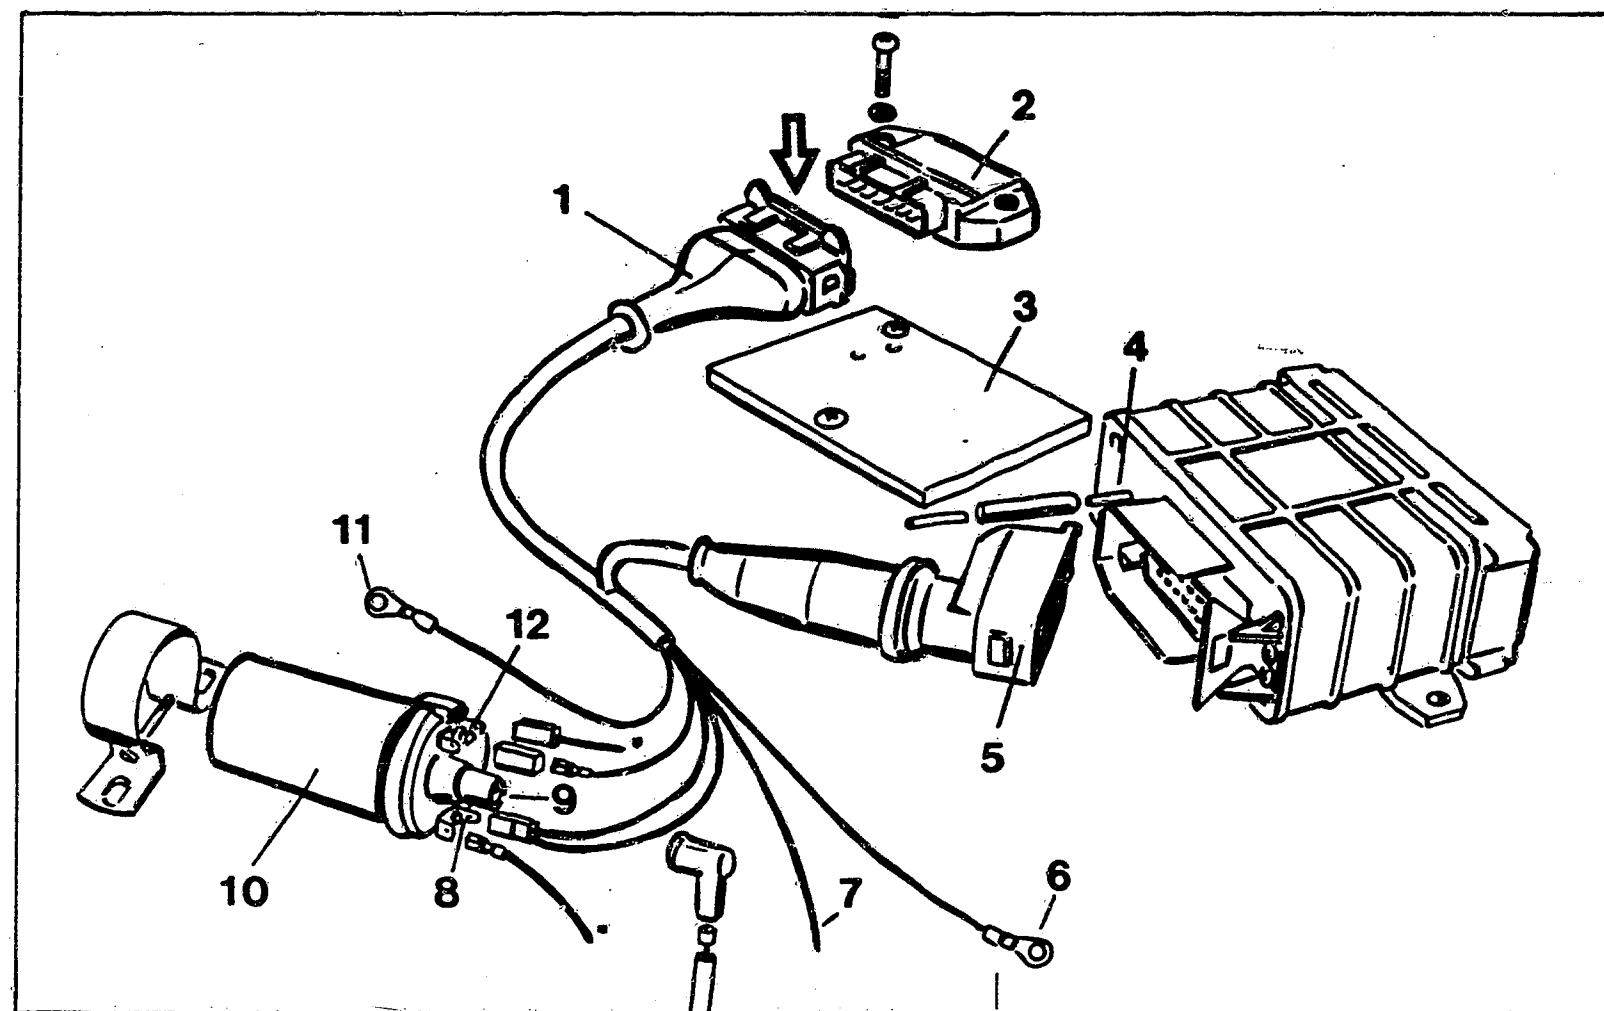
Schaltgerät, Steuergerät und ihre Verkabelung. 1 Anschlussstecker – 2 TSZ-H-Schaltgerät – 3 Kühlplatte – 4 Unterdruckanschluss am Steuergerät – 5 Anschlussstecker (zum Abziehen Drahtsicherung drücken) – 6 Massekabel des TSZ-H-Schaltgeräts – 7 Kabel zum Zündverteiler – 8 Klemme 15 (+) – 9 Klemme 4 – 10 Zündspule – 11 Masse des VEZ-Steuergeräts – 12 Klemme 1.
